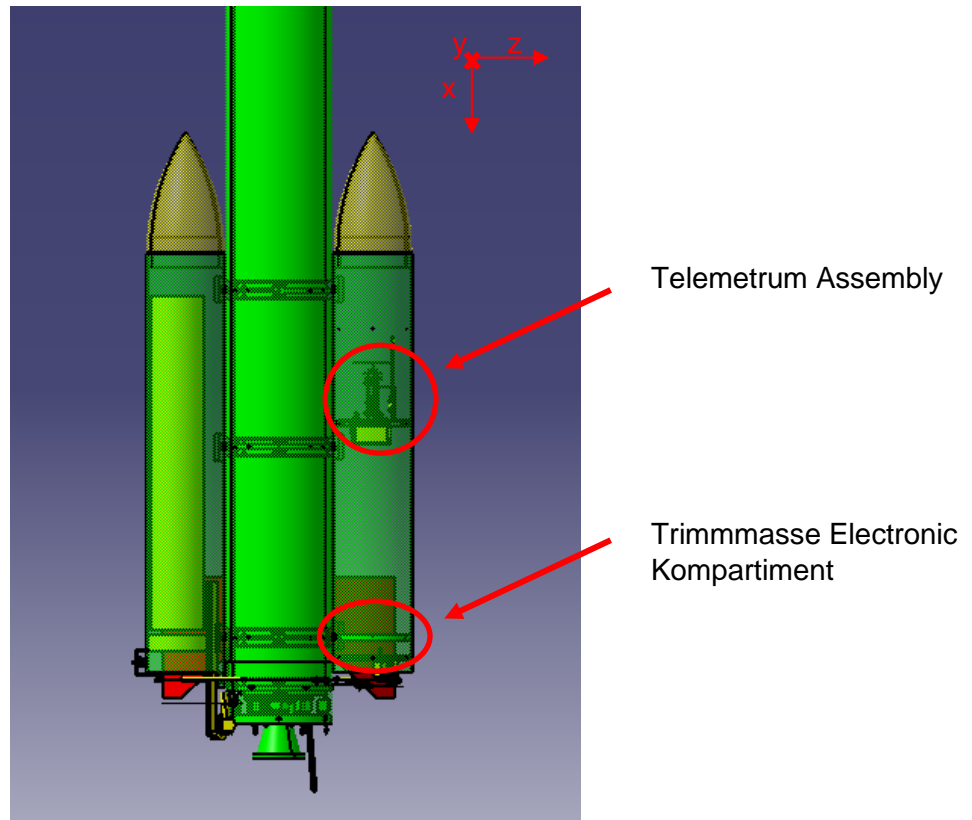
Variante 2 – Versetzen der Telemetry Assembly
